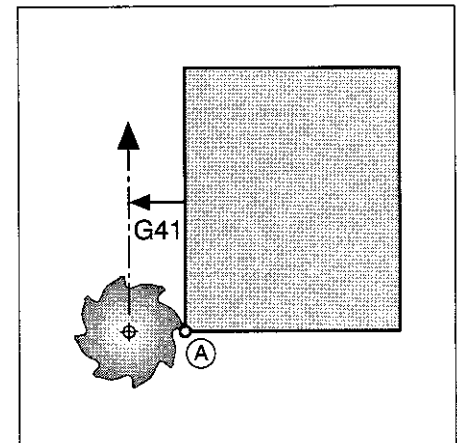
Erster Konturpunkt einer Bearbeitung
